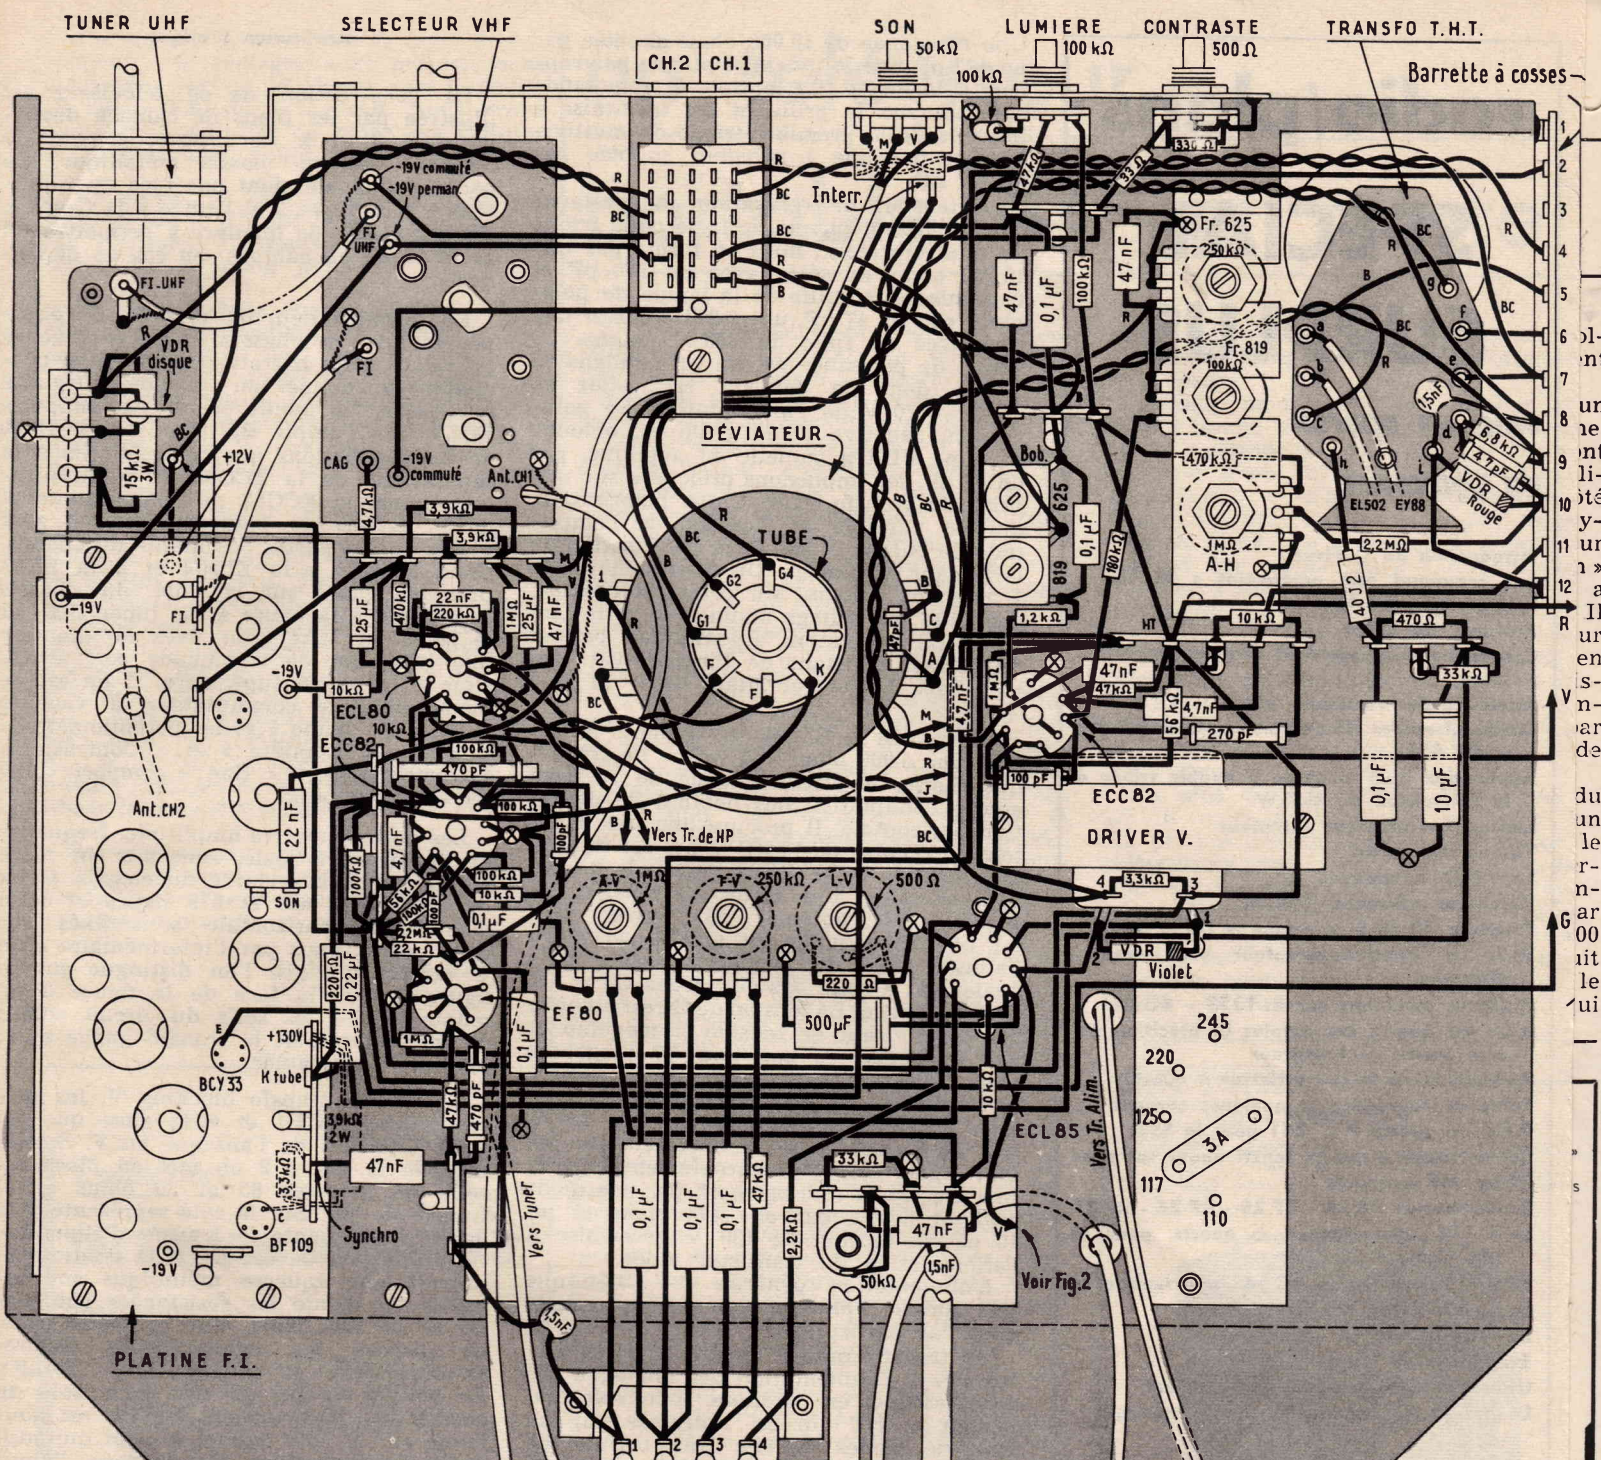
CABLAGE ARRIERE DU CHASSIS
